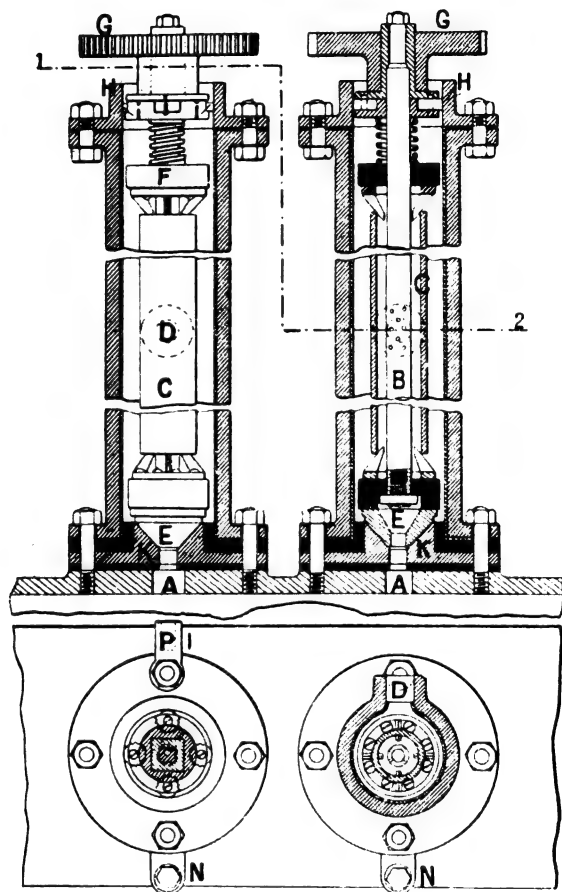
à 4. — Coupes verticales; coupe horizontale par le plan 1; coupe horizontale par le plan 2.
